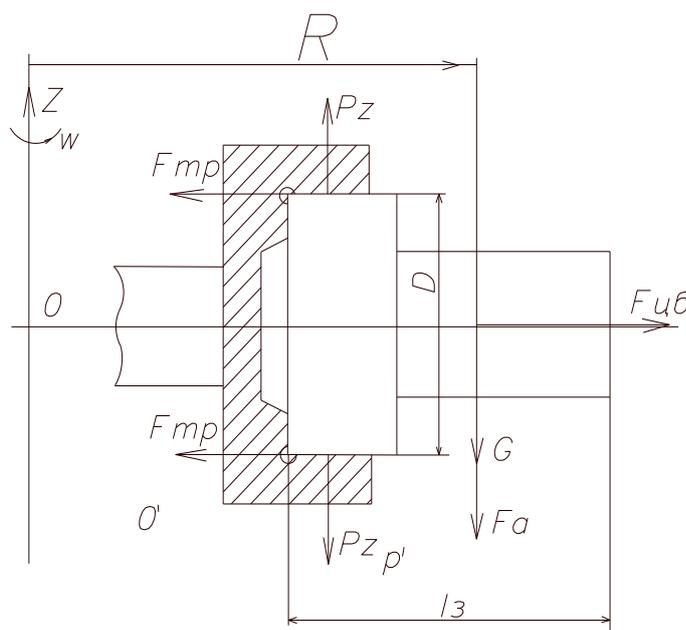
расчетная схема для определения усилия закрепления заготовки в схвате ПР
